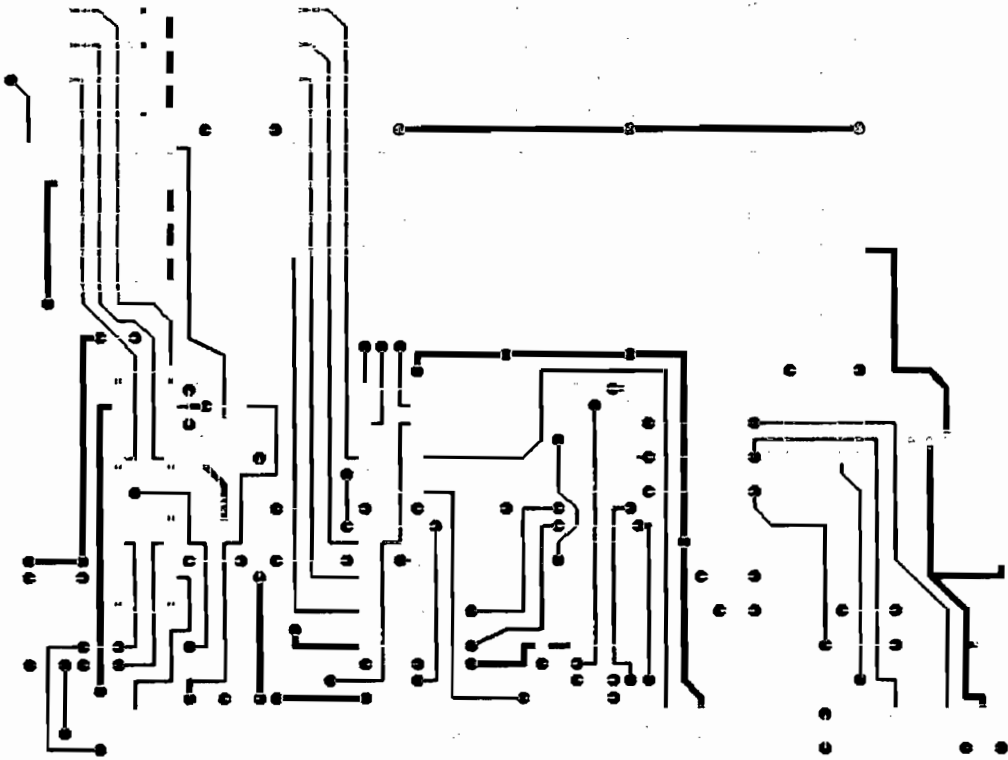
Tarjeta de visualización, lado de soldadura.
